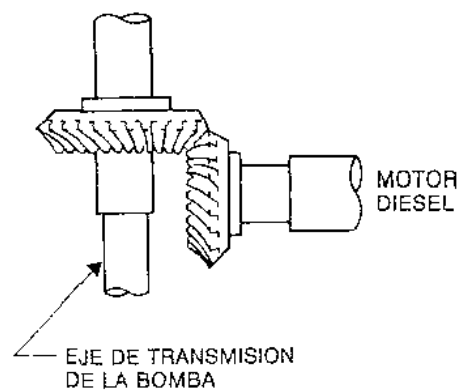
Engranaje entre el eje de transmisión de la bomba y el eje del motor Diesel.
